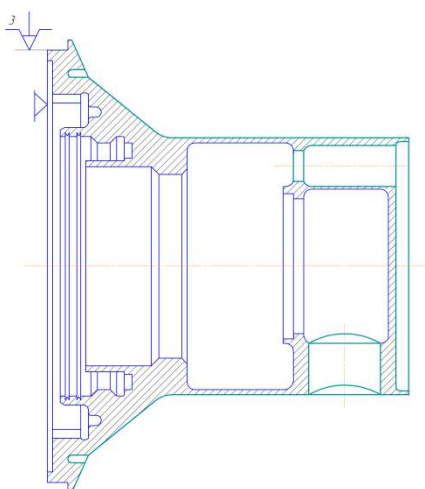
Схема базирования заготовки на 005 комплексной операции с ЧПУ (установ 2)
